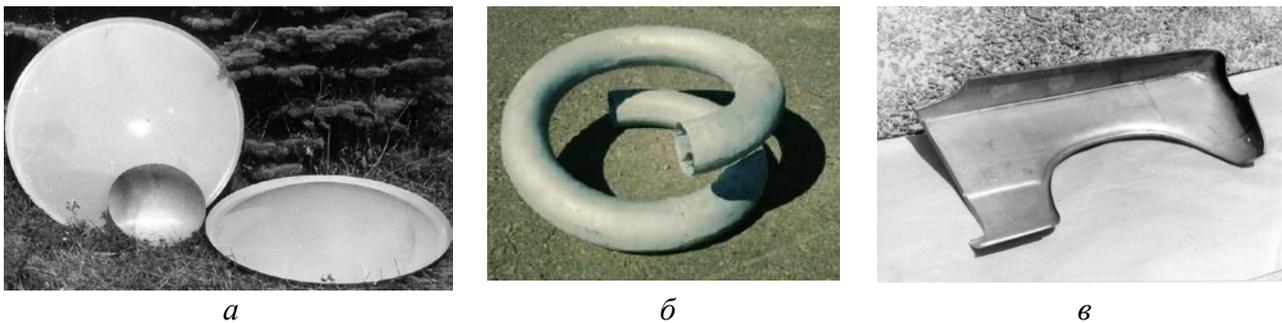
Внешний вид деталей, изготовленных на прессе ПЭГ-ХАИ-500:
